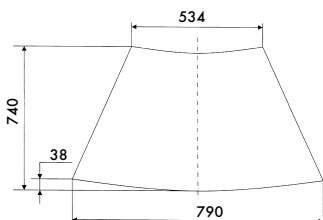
Развертка деталей № 1, 41 обшивки обтекателя
